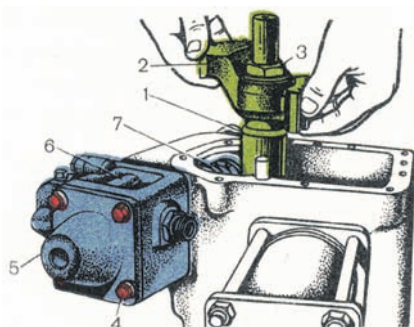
Снятие поворотного вала и червяка. 1 — поворотный вал; 2 — сектор; 3 — гайка; 4 — болт; 5 — крышка; 6 — распределитель; 7 — червяк
